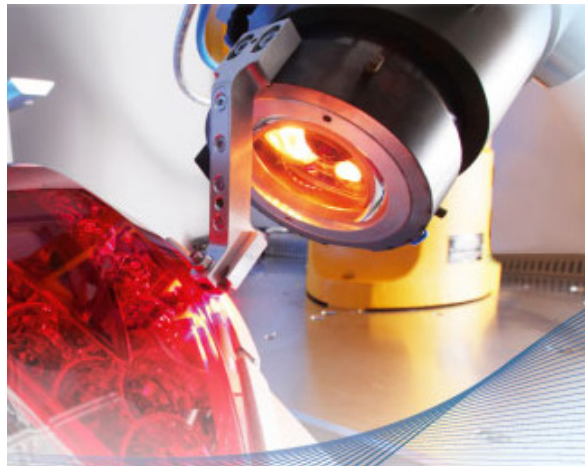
Acción de la roldana sobre los elementos a soldar (Fuente: modificada de LPKF).
